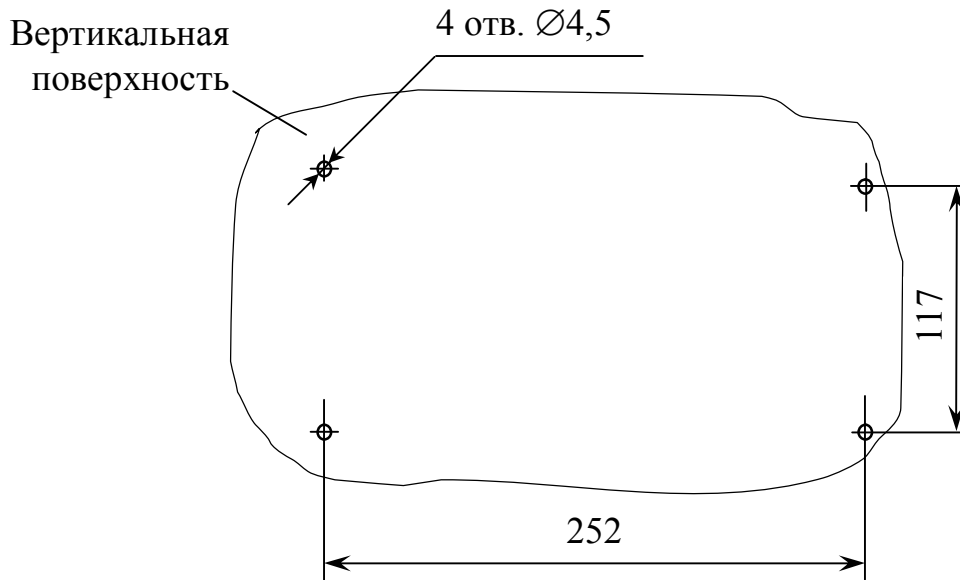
Расположение отверстий для крепления блока преобразовательного щитового исполнения
